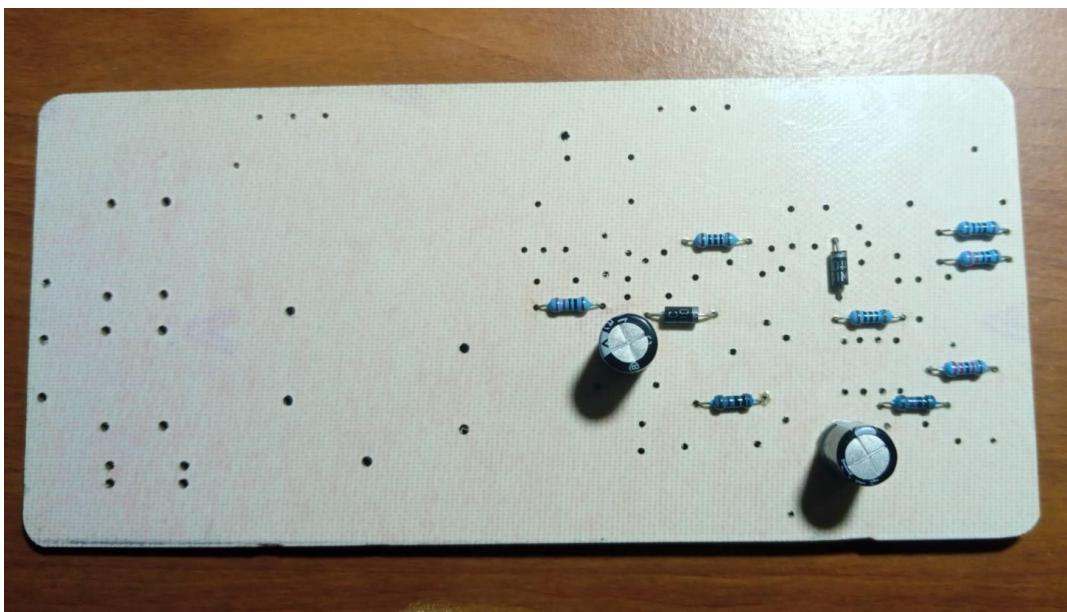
Primer grupo de componentes soldados a la PCB.
